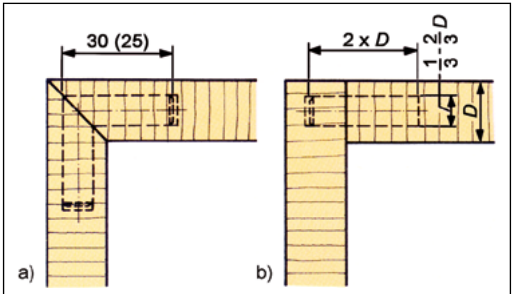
Gedübelte Korpuseckverbindungen (Schnitte) a) auf Gehrung gedübelt, b) stumpf gedübelt
